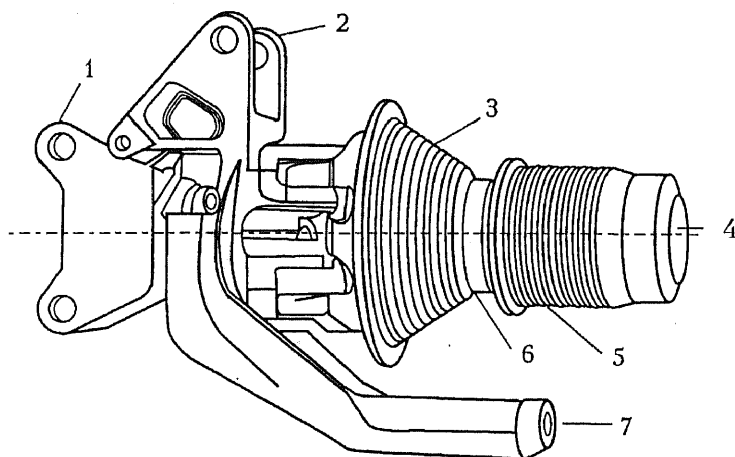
Втулка несущего винта с эластомерными подшипниками (вертолет УН-60А):
